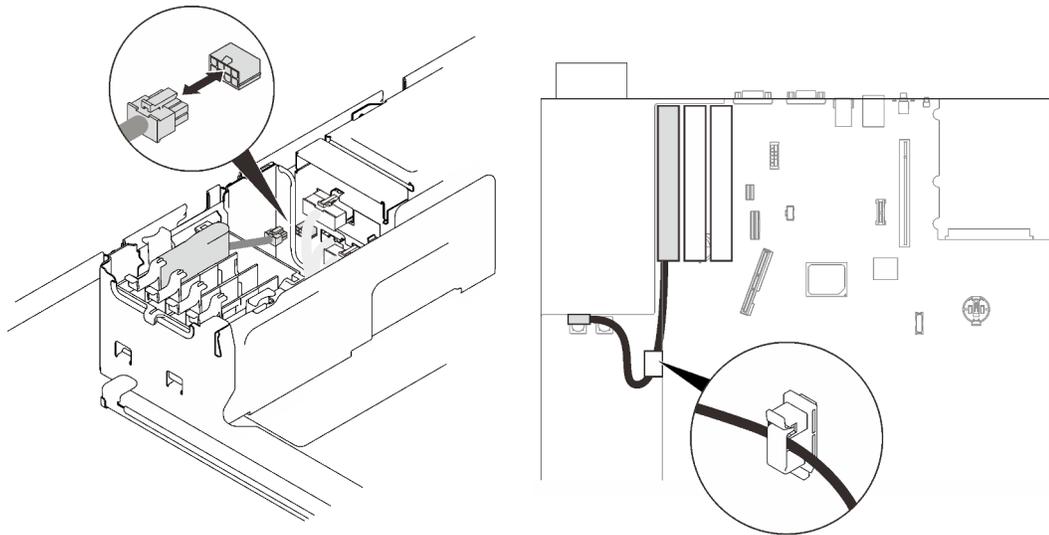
Scollegamento del cavo del modulo di alimentazione flash
